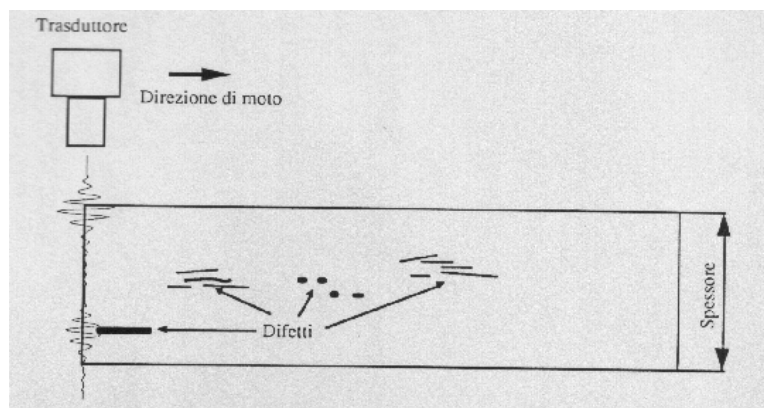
a – Tecnica B-scan con vista frontale -
